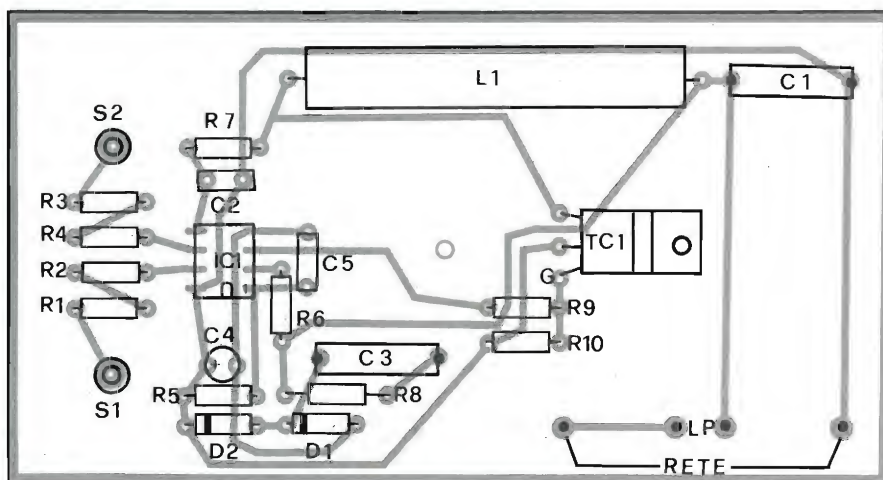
Disposizione pratica dei componenti del dimmer.
